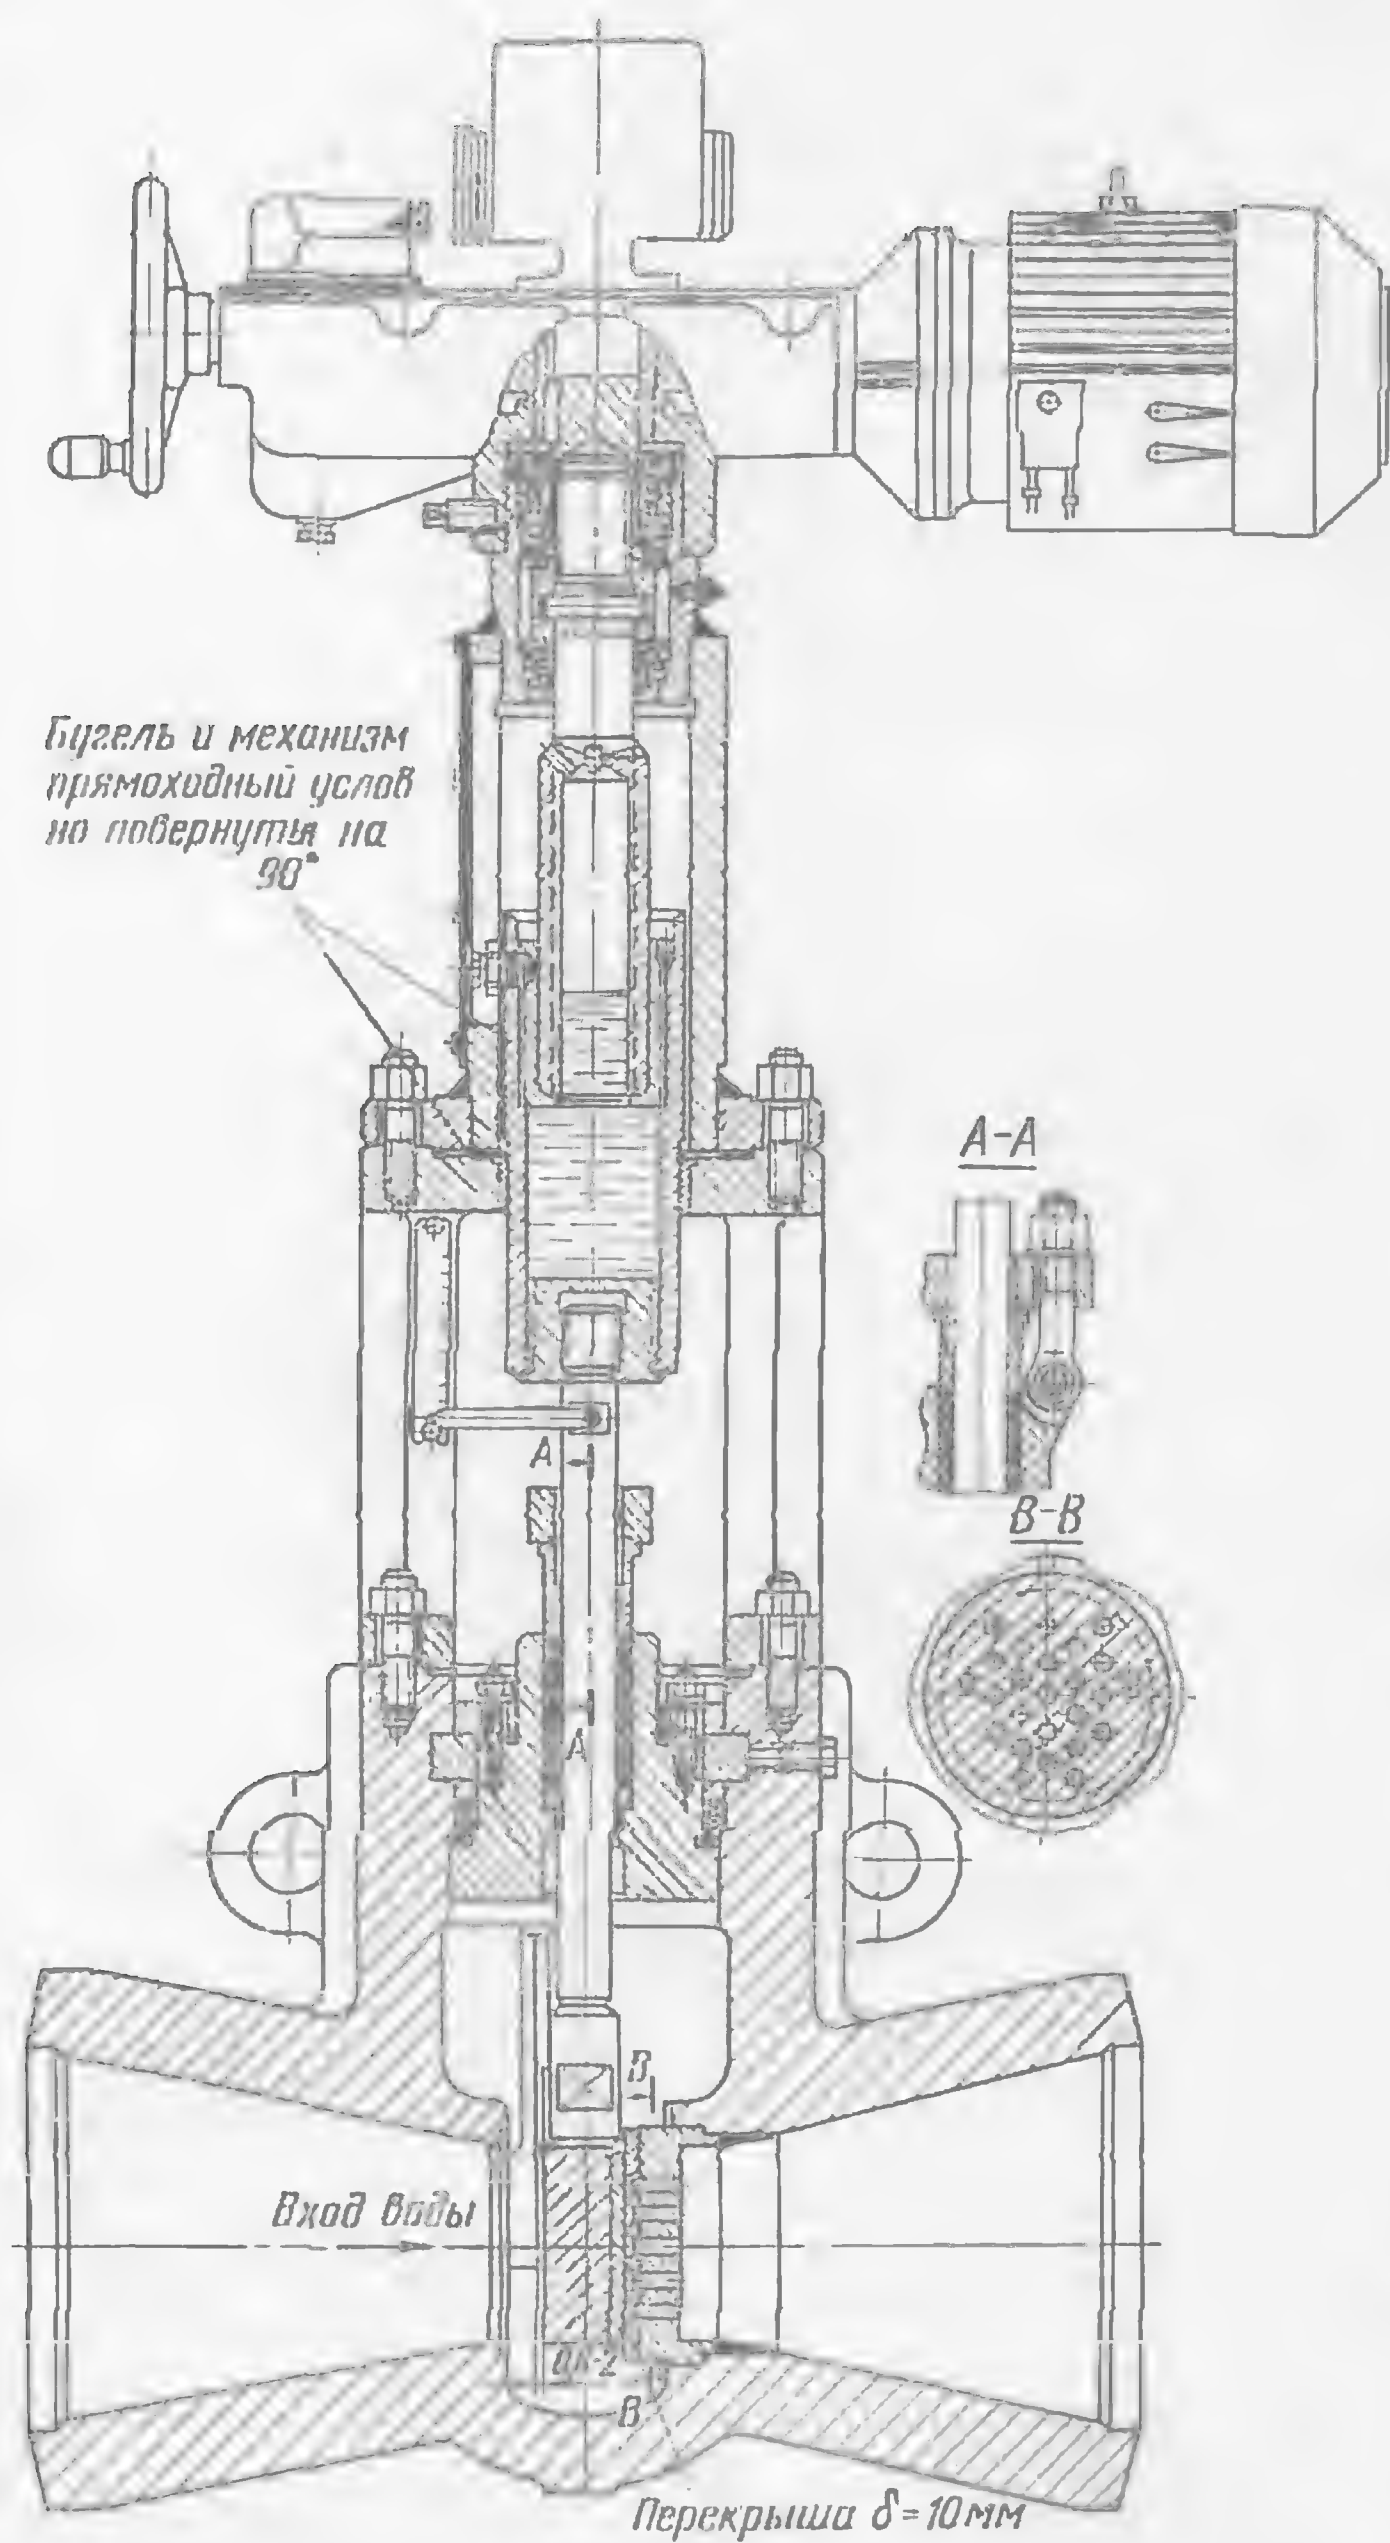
Регулирующий питательный клапан шиберного типа конструкции ВАЗ с профилем в седле.
